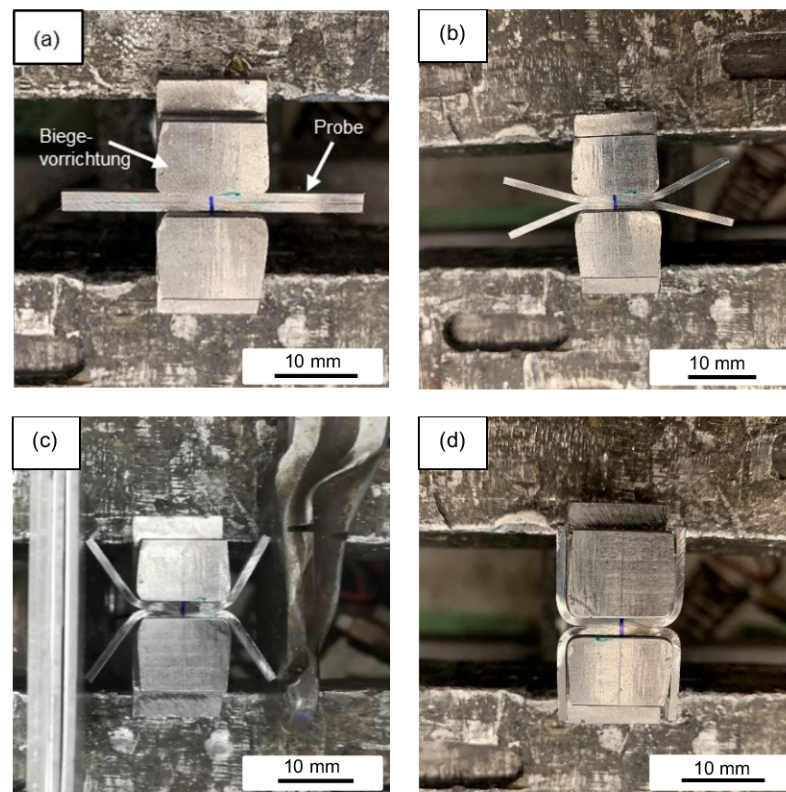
Formgebung der Proben: (a) Einspannen der Probe in die Biegevorrichtung, (b) Auseinanderdrücken der Bleche mit einem Flachmeißel, (c) nach dem Ziehen mit einer Rohrzanze wurde die Probe (d) mit einer Schraubzwinde in die Endform gebogen.
